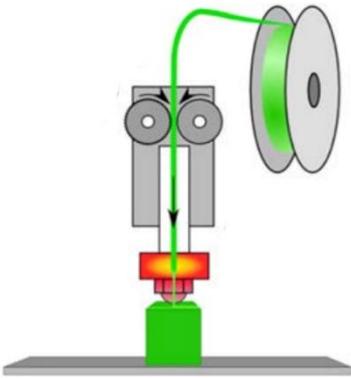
Funcionamiento de una máquina de manufactura por extrusión y deposición aditiva.
